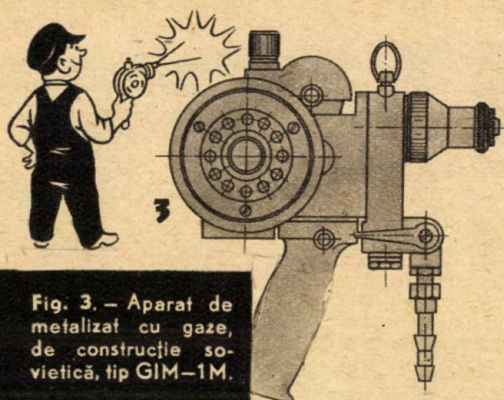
Aparat de metalizat cu gaze, de construcție sovietică, tip GIM-1M.
